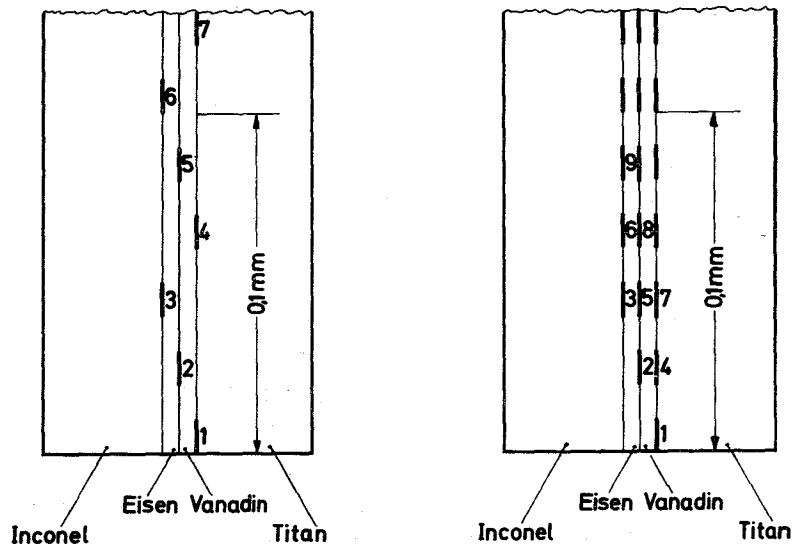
+b Impulsfolge beim gleichzeitigen Ausführen mehrerer Schweißnähte
